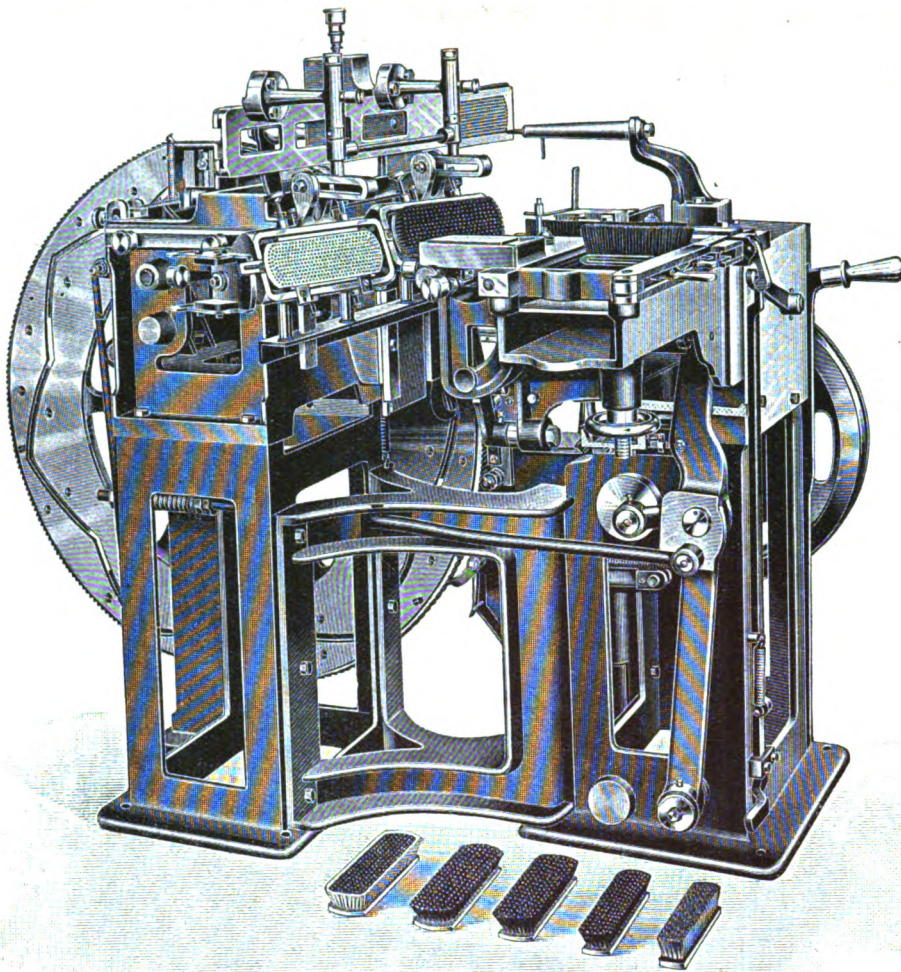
Automatische Bohr- und Einstanzmaschine.
